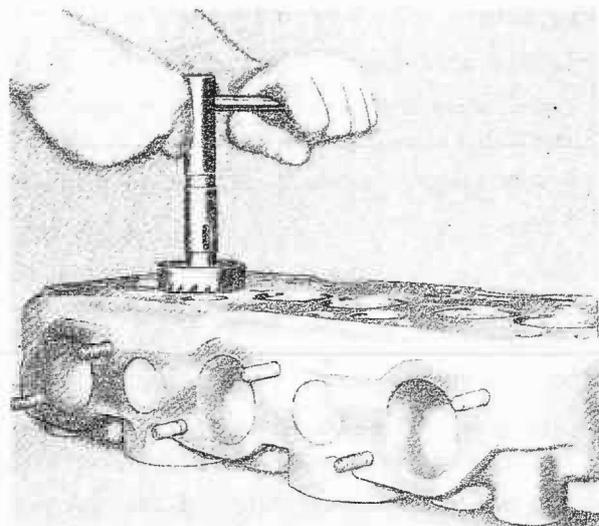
Fräsen der Ventilsitze (45°) mit handelsüblichen Ventilfräser
